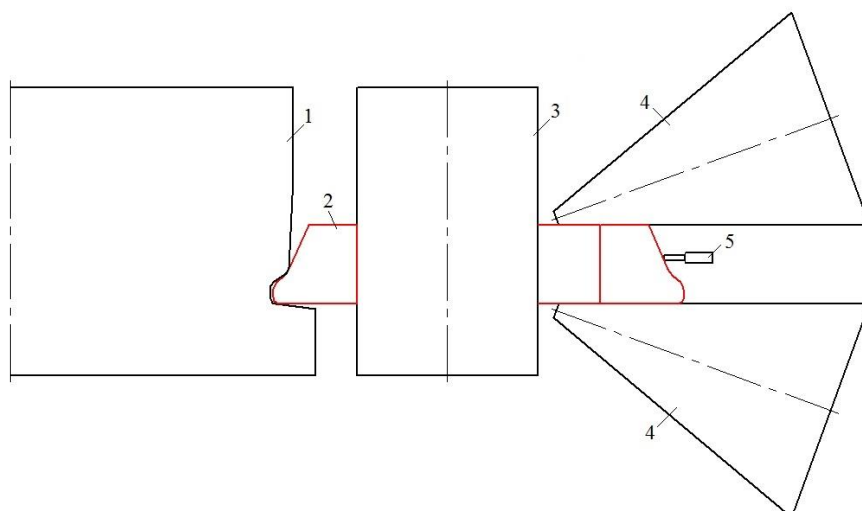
Схема радиально-осевого кольцепрокатного стана: 1 – главный приводной валок; 2 – прокатываемое кольцо с наружным гребнем; 3 – валок-оправка; 4 – наклонные (конические) валки; 5 – устройство для измерения наружного диаметра кольца
